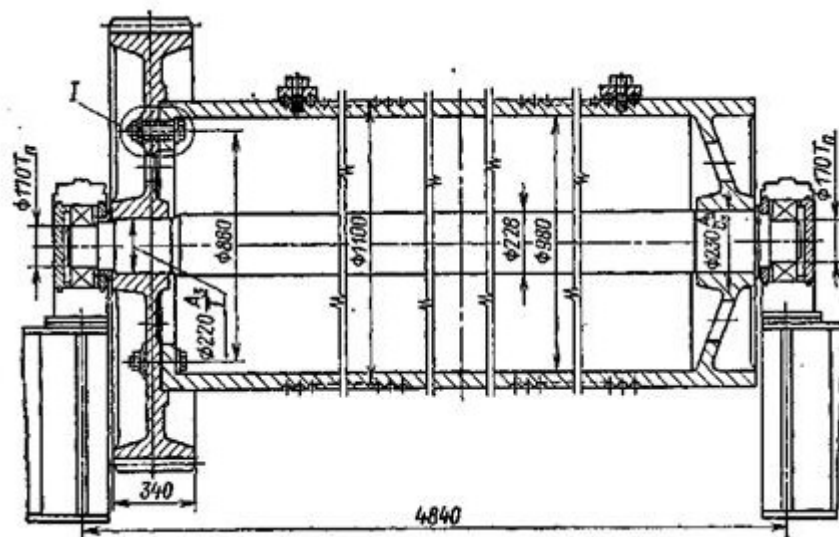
Барабан с открытой зубчатой передачей
